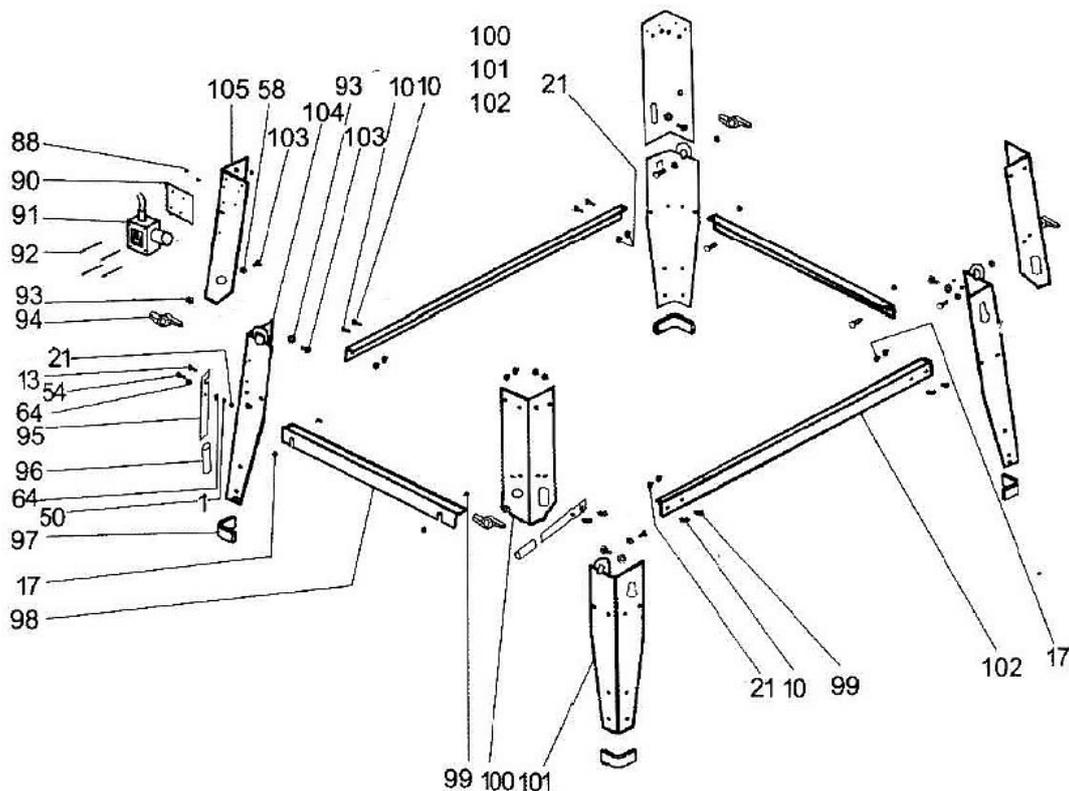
Plan des pièces détachées 3 - Scie de table TKS 316 PRO
